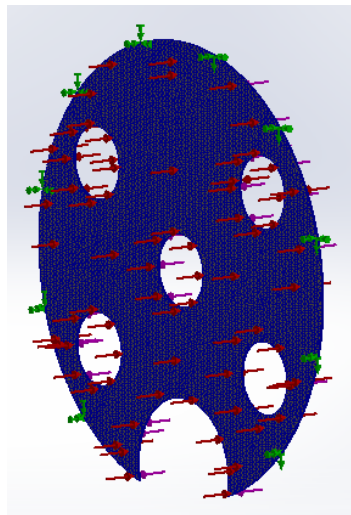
Mallado del rompeolas plano tipo 1 para su posterior análisis estático
